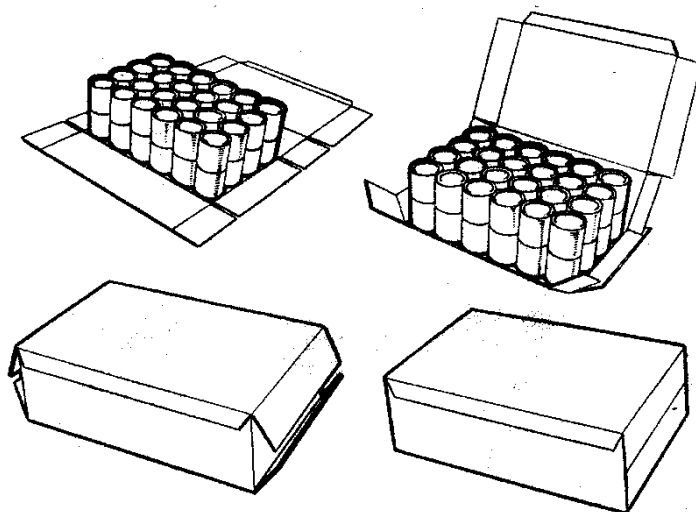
Упаковка консервных банок по способу оборачивания
